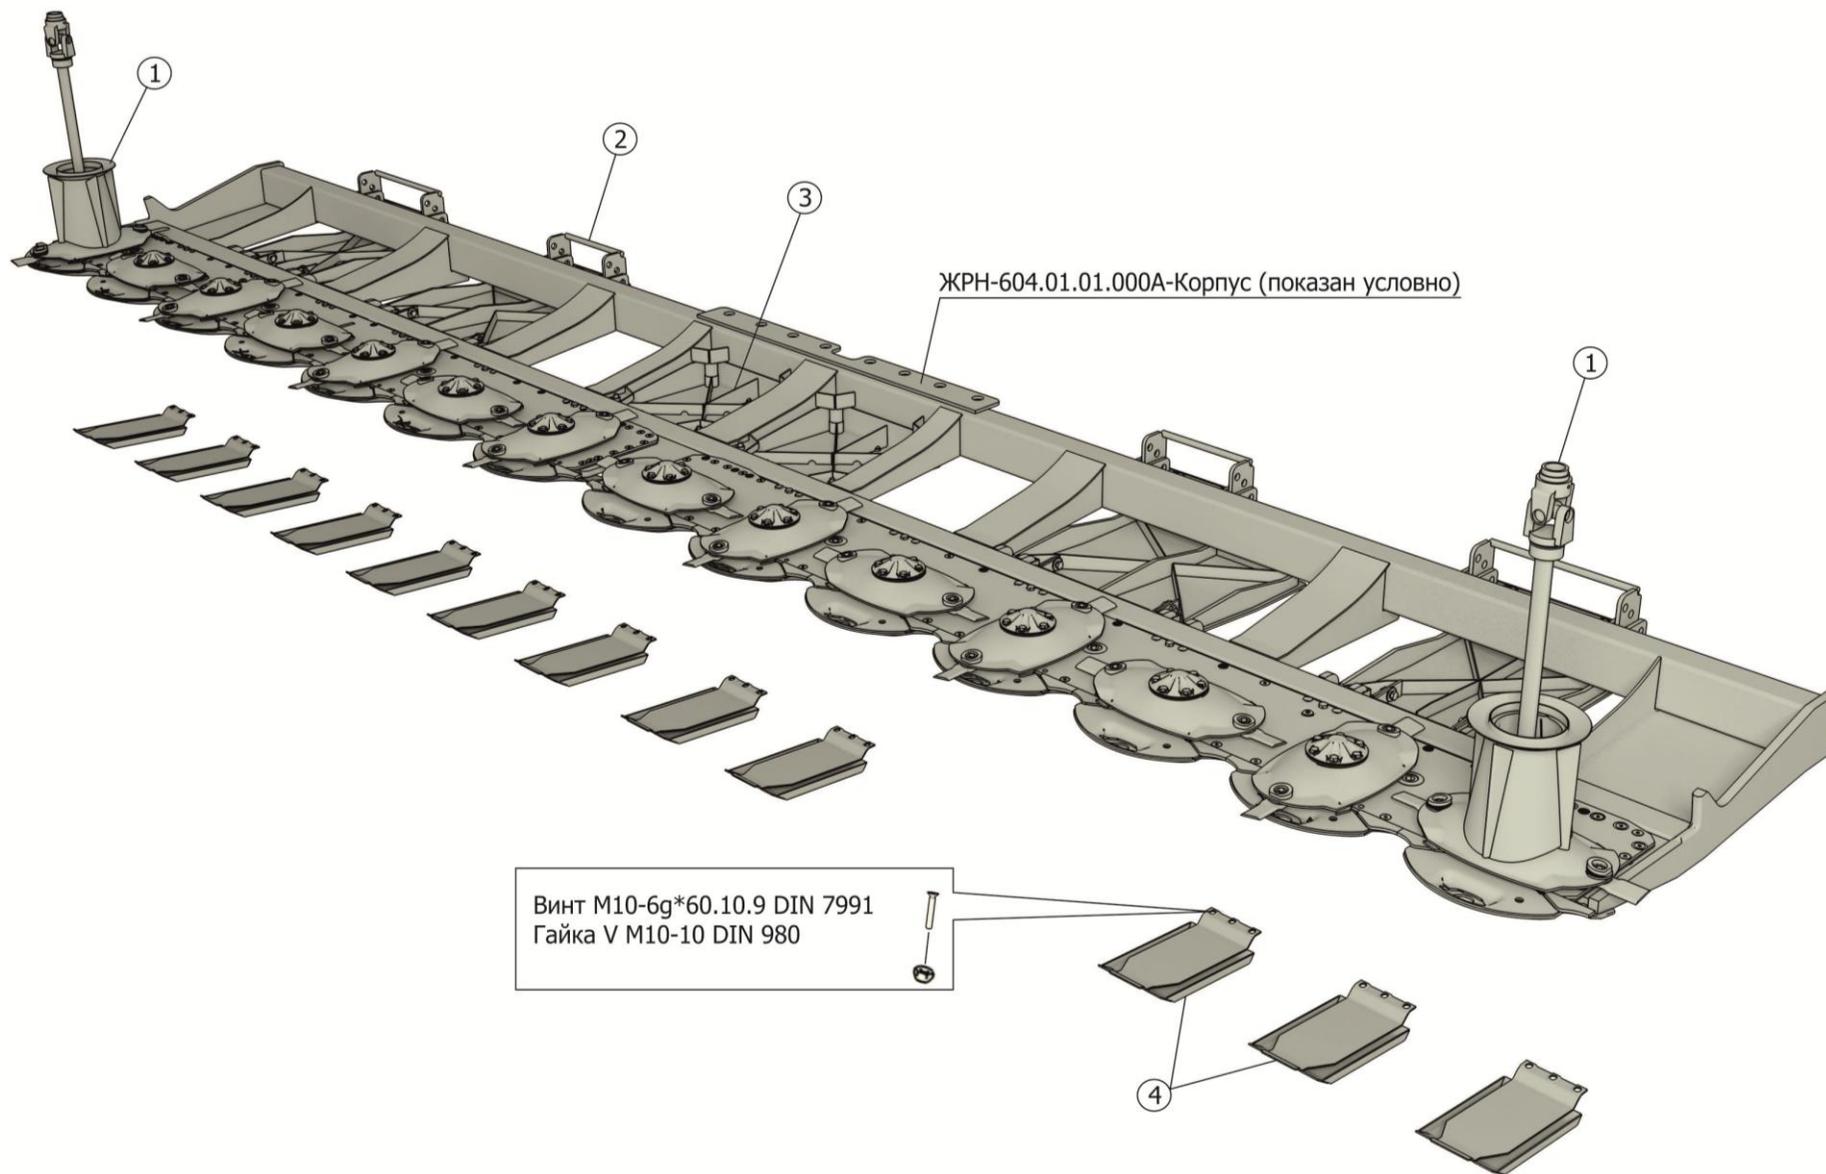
Установка брусьев режущих и башмаков опорных ЖРН-604.04.00.000А
